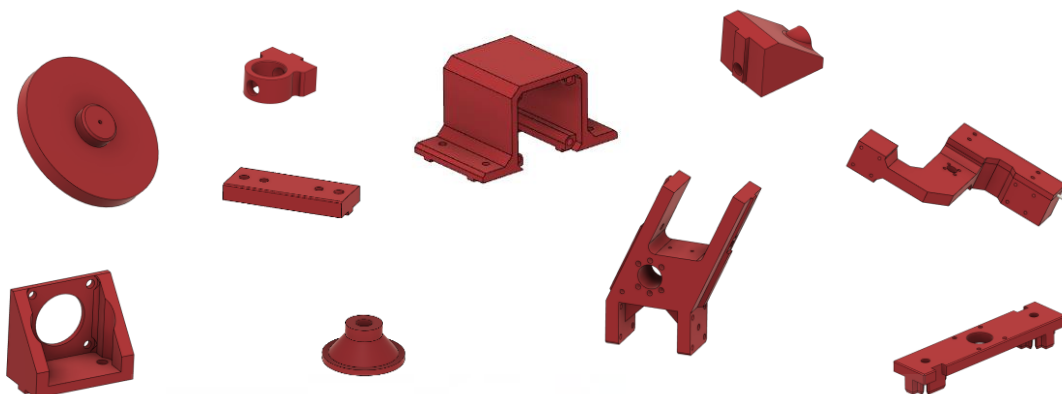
Conjunto de piezas diseñadas para la bobinadora.
